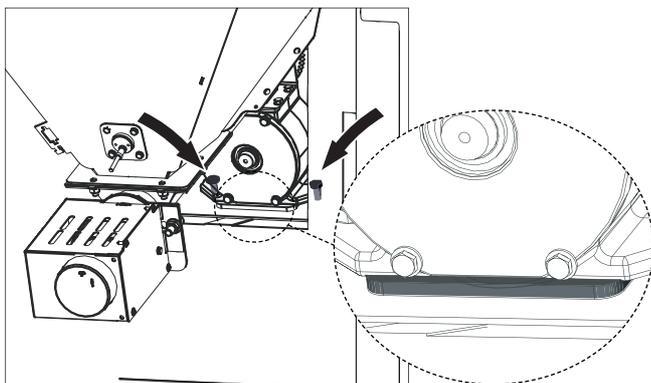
Serrare uniformemente entrambe le viti sull'unità tubo della coclea valvola rotativa; la sporgenza della guarnizione deve essere uniforme su tutto il perimetro
